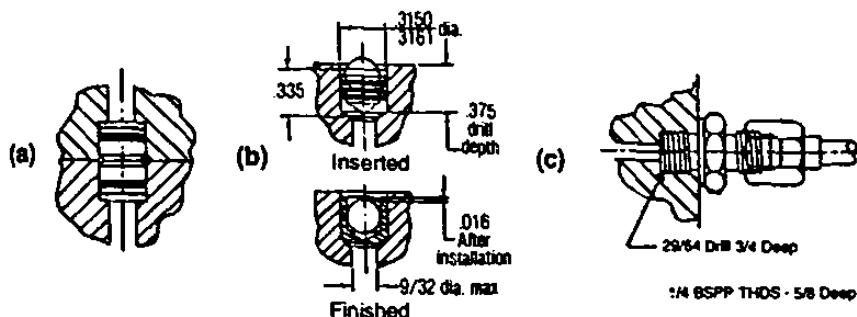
El accesorio (c) se monta usualmente al final de un pasaje hidráulico. Este tipo de sujetador puede ser usado por si solo o servir como un conector de rápido desmontaje.
